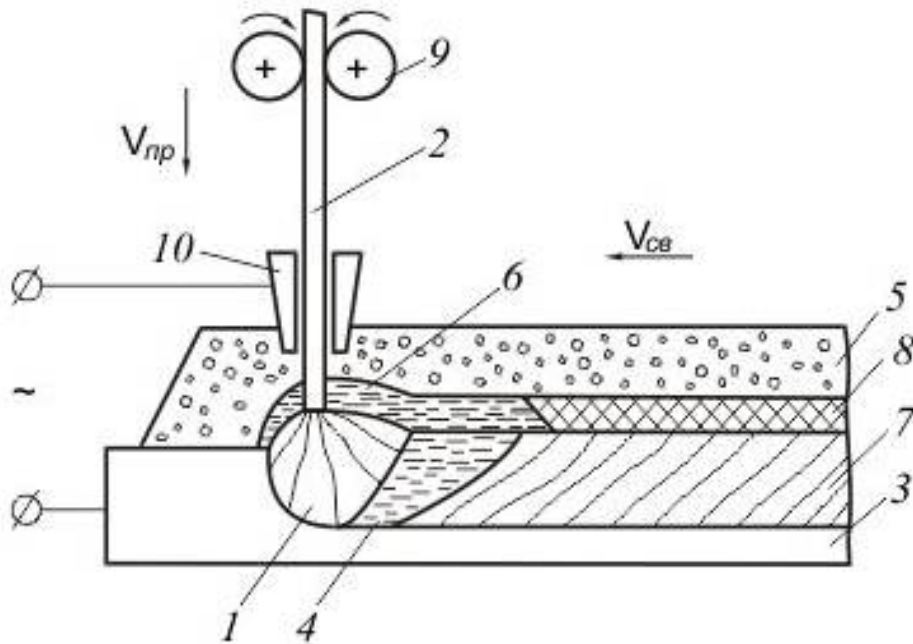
Схема процесса автоматической дуговой сварки под флюсом
